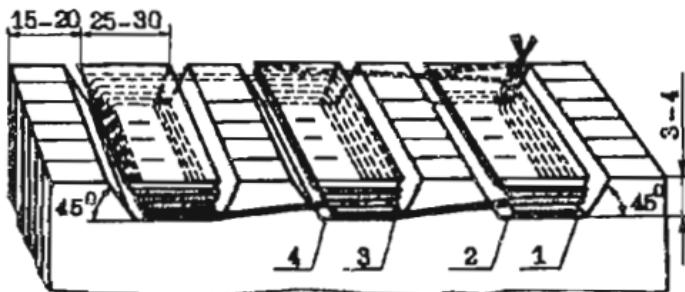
Усиление корешка книжного блока с бесшвейным креплением путем обмотки его прочной нитью: 1-2 и 3-4 - пазы в корешке блока, образующие «ласточкин хвост»
